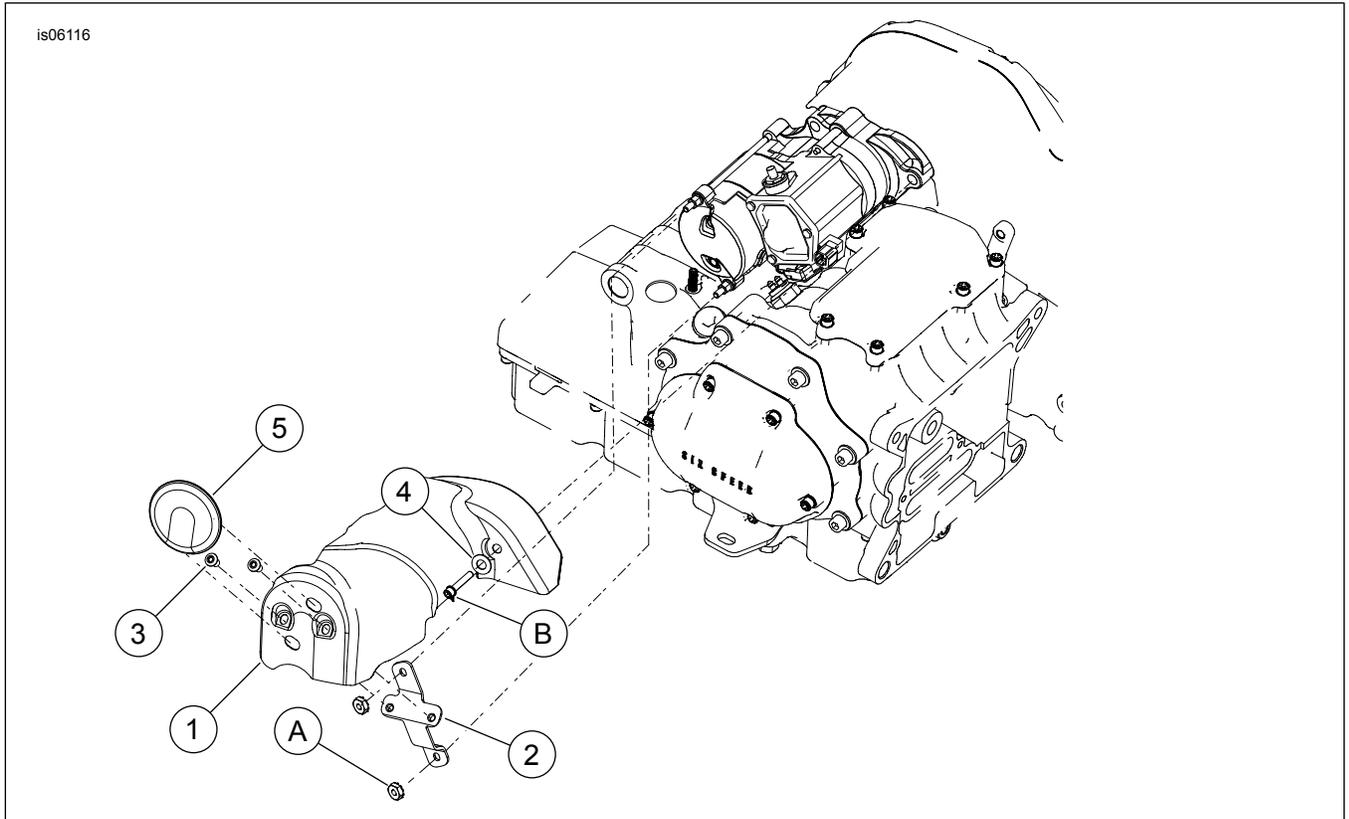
Pièces de rechange : Couvercle du démarreur Touring
